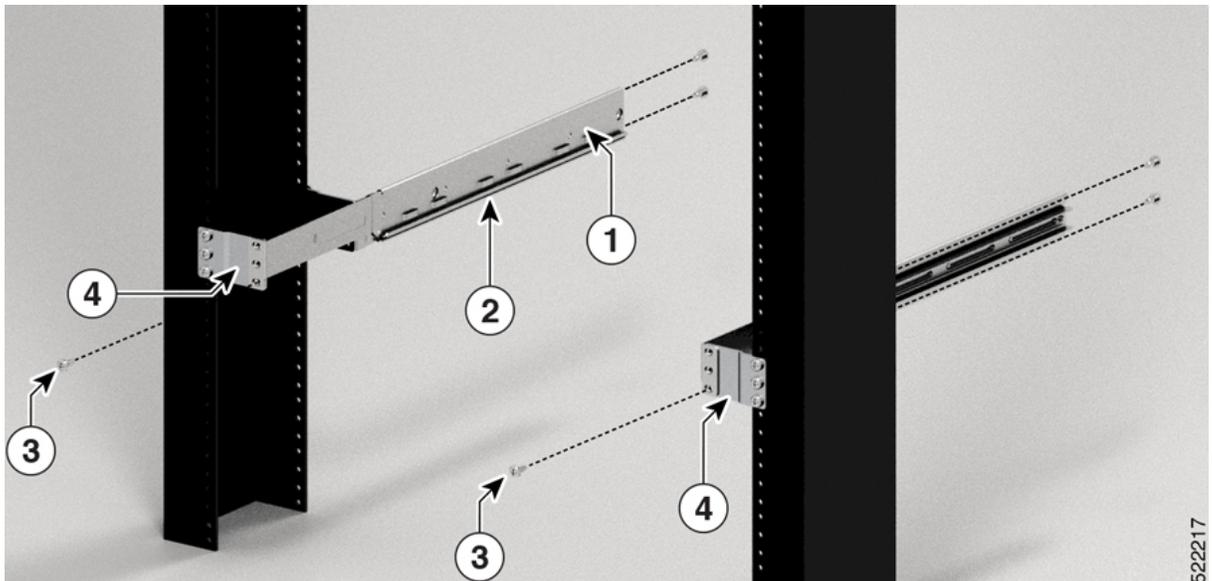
Assemblage du rail coulissant pour montage sur un rack de 19 pouces à 2 montants
